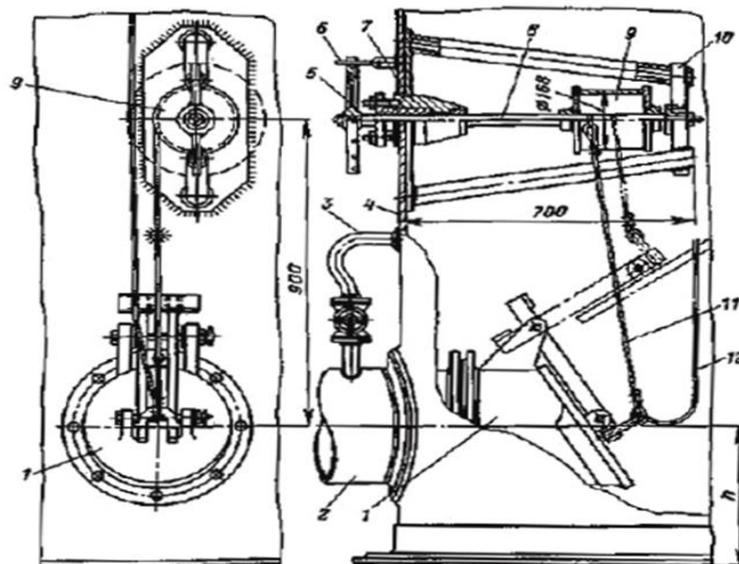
Механізм бокового управління хлопашкою РВС: 1 – хлопашка; 2 – приемо-роздаточний патрубок; 3 – перепускная труба с вентилем;
